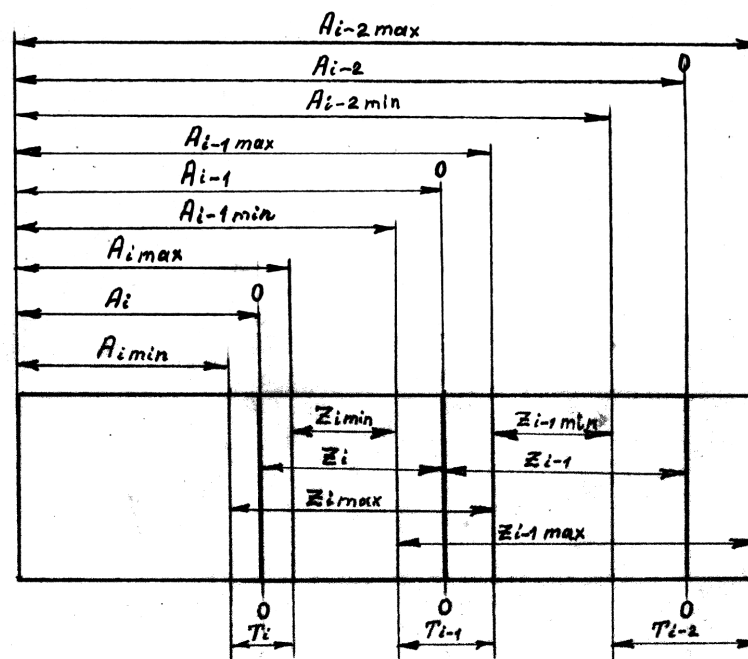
Схема розмірів, припусків і допусків заготовки до операційних переходів та розмірів і допусків готової деталі:
